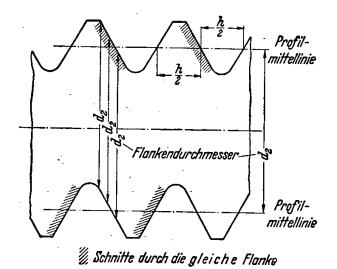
Begriffsfestlegung des Flankendurchmessers d_2 als diametraler Abstand der Flanken
